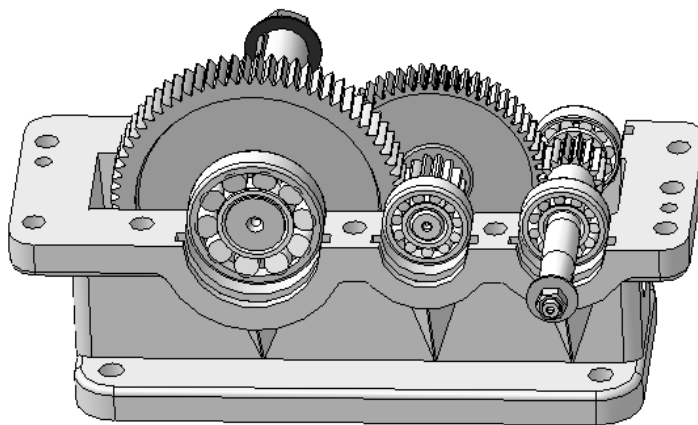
Валы, установленные в корпусе редуктора на подшипниках качения
